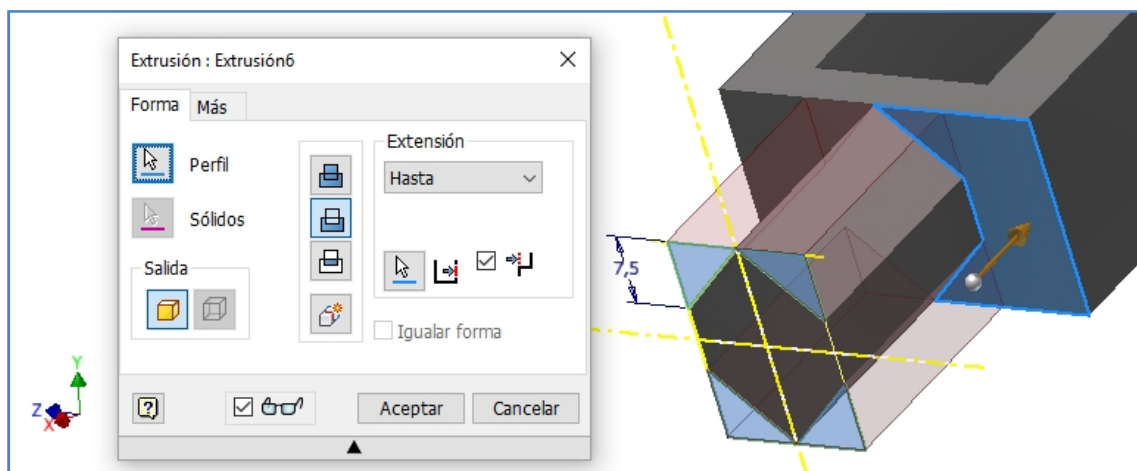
Cuarta extrusión, que es similar a la quinta solo que en el otro lado del sólido.
